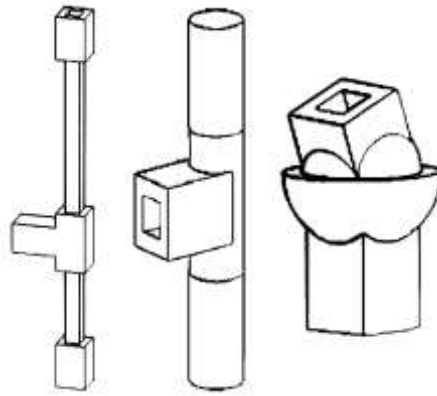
Лінійний, поворотний та шаровий з'єднання
